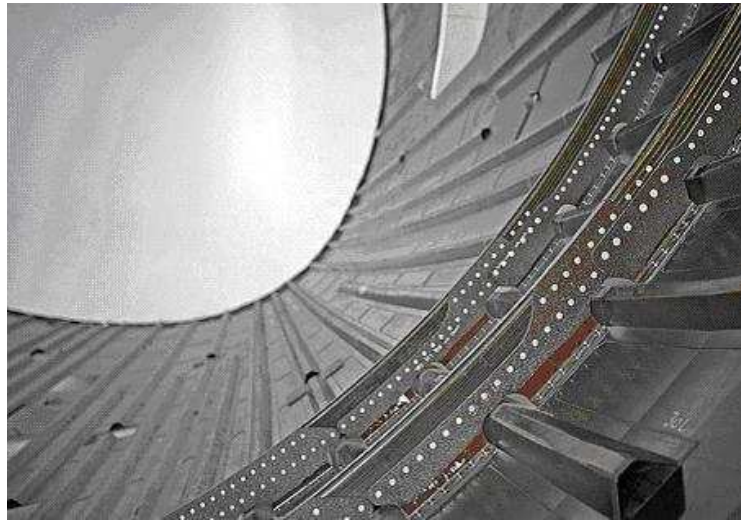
Section de fuselage désassemblé du Boeing 787 Dreamliner, en matériaux composites [3].
